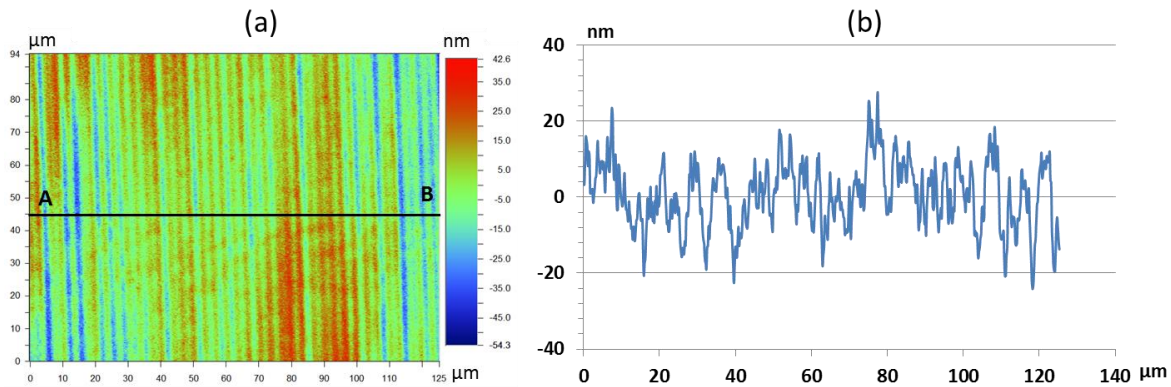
a) Oberflächenmessung des Werkzeugeinsatzes nach der Fly-Cutting-Bearbeitung mittels WLI, b) extrahiertes 2D-Profil entlang von AB [32]
